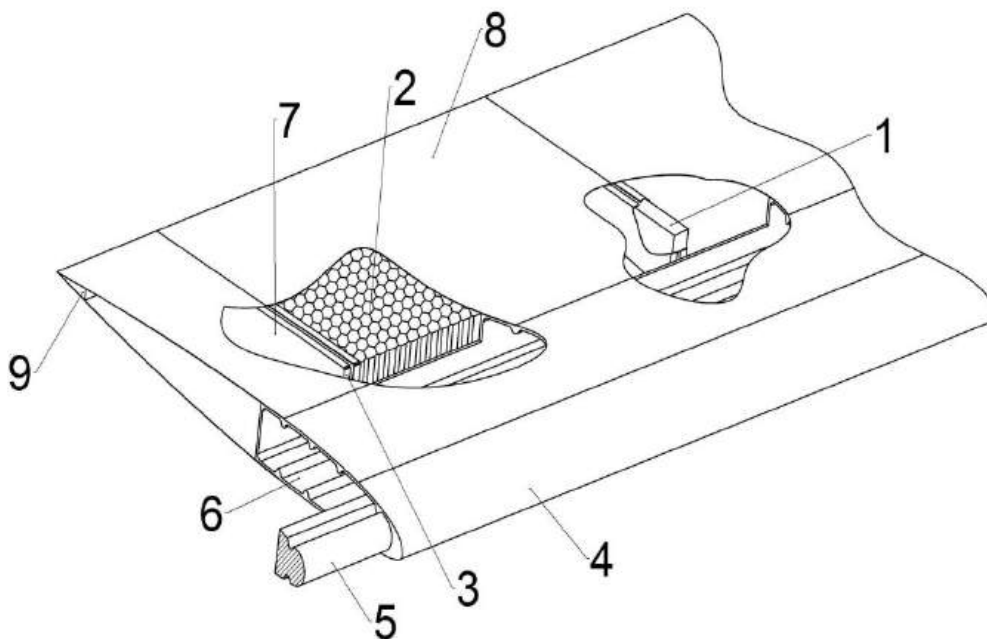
Конструктивно-силова схема металевої лопаті:
